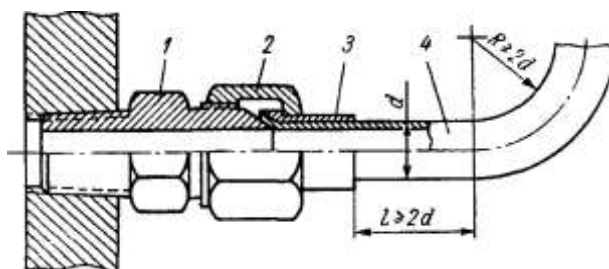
Типовое соединение трубок со штуцером (1 - штуцер; 2 — накидная гайка; 3 — промежуточная втулка; 4 — трубка)
